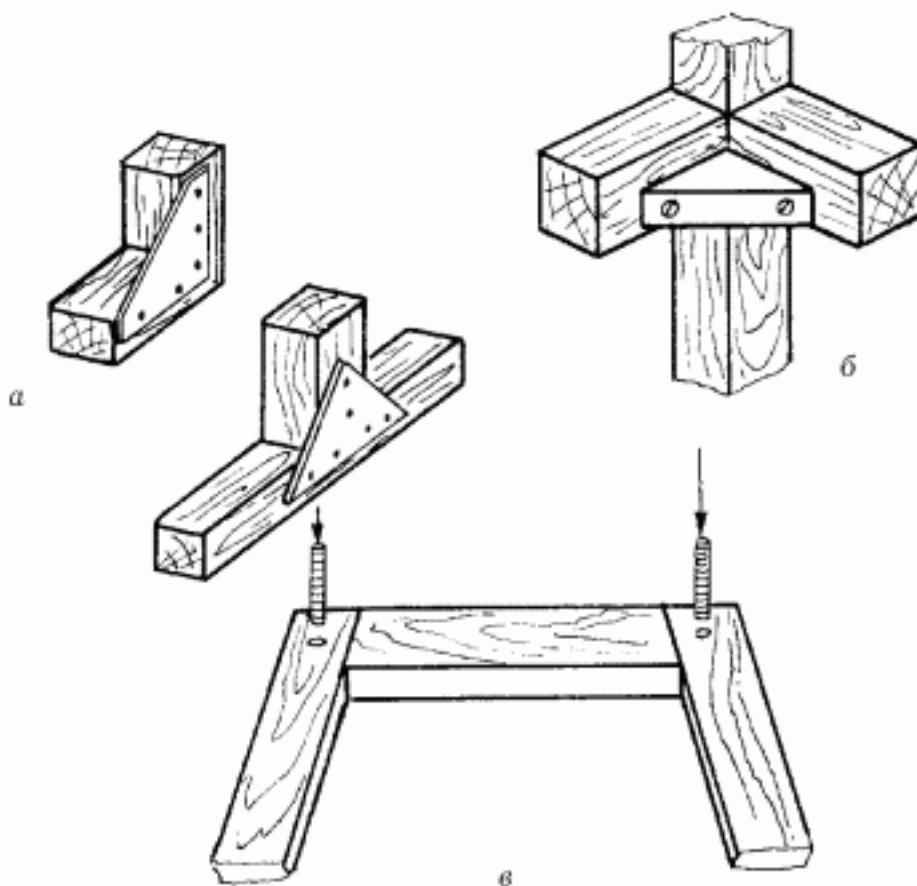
Дополнительное крепление конструкции: а – угольниками; б – бобышками; в – нагелями.
